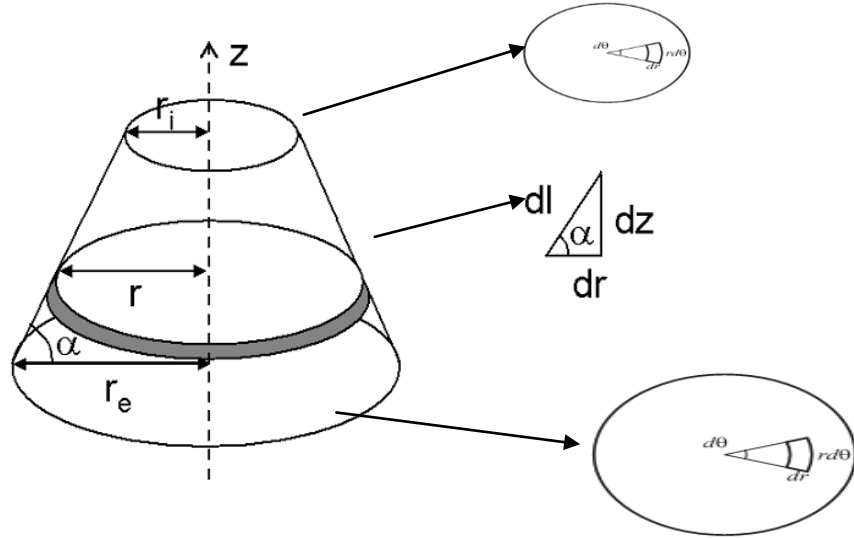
Zones infinitésimales de contact entre l'outil du soudage et la pièce [Bastier.24].
